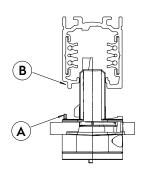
Chiave meccanica Pic. 3 Mechanical key
